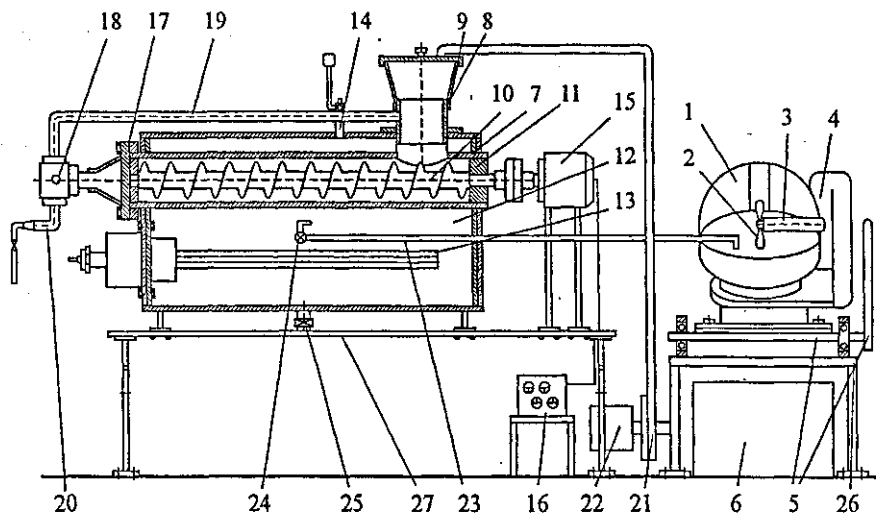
Установка для изготовления твердых стержней пенообразователей
